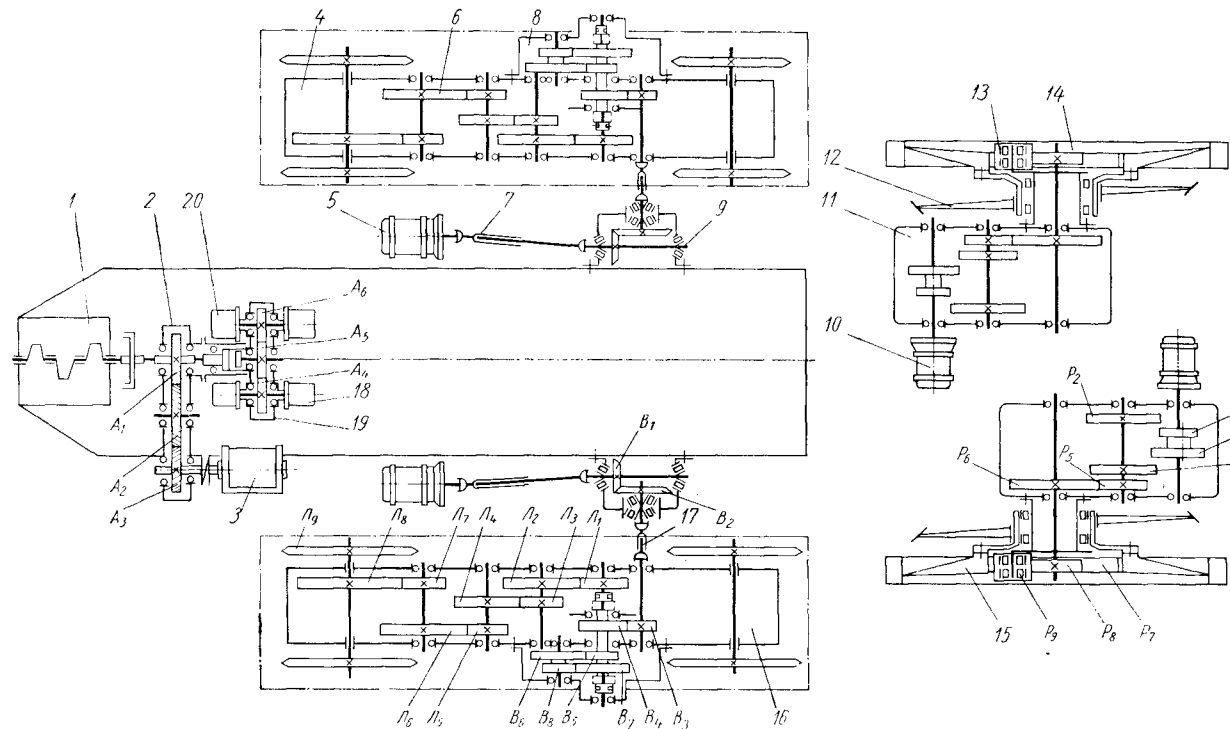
Кинематическая схема силовой передачи экскаватора-каналокопателя Д-583:
